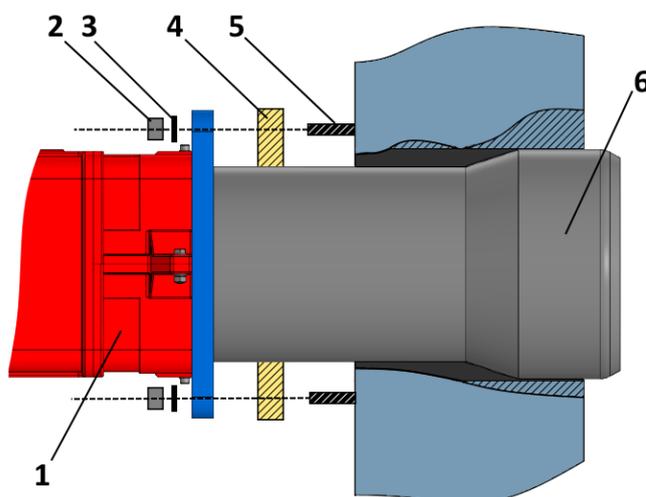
Пример монтажа горелки к топке. 1 – Горелка; 2 – Крепежная гайка; 3 – Шайба; 4 – Теплоизоляционный уплотнитель; 5 – Шпилька; 6 – Сопло.
